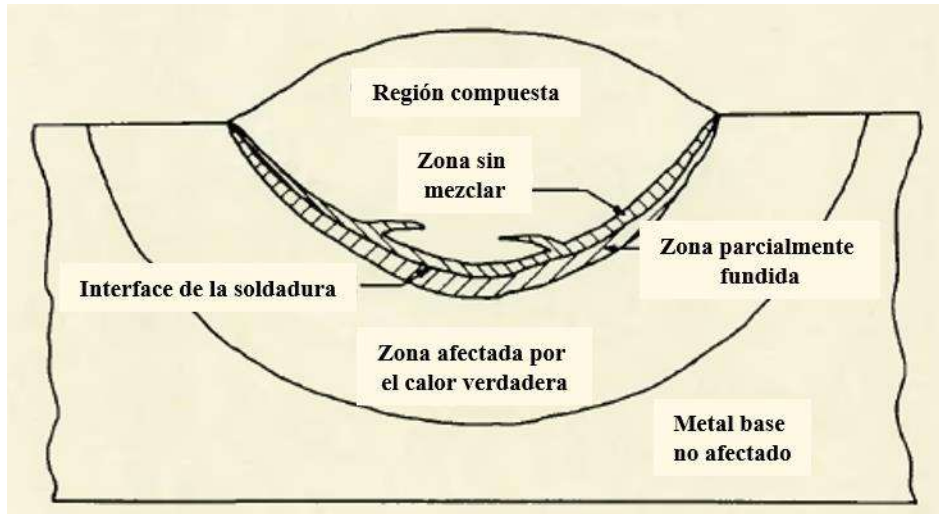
Ilustración esquemática que muestra las regiones de una soldadura [72].
